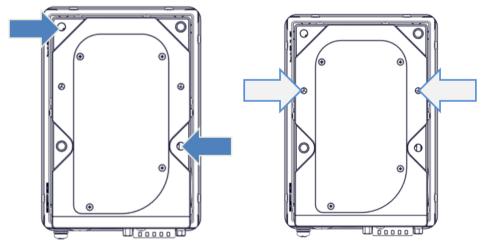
Ansicht Unterseite: Lage der Gewindebohrungen zur Befestigung des Positionierers von unten (links); Lage der Bohrungen für Passstifte (rechts)
